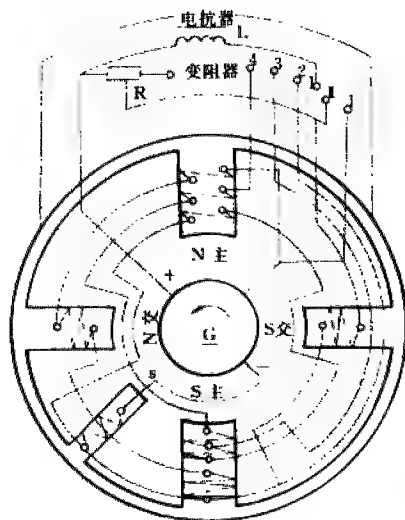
AX1-165 型直流焊接发电机电气线路图
